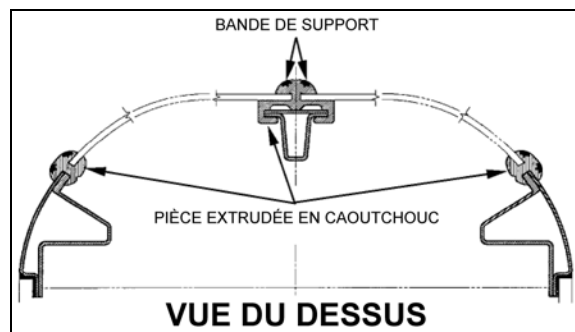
VUE EN PLAN DE L'INSTALLATION DU PARE-BRISE
